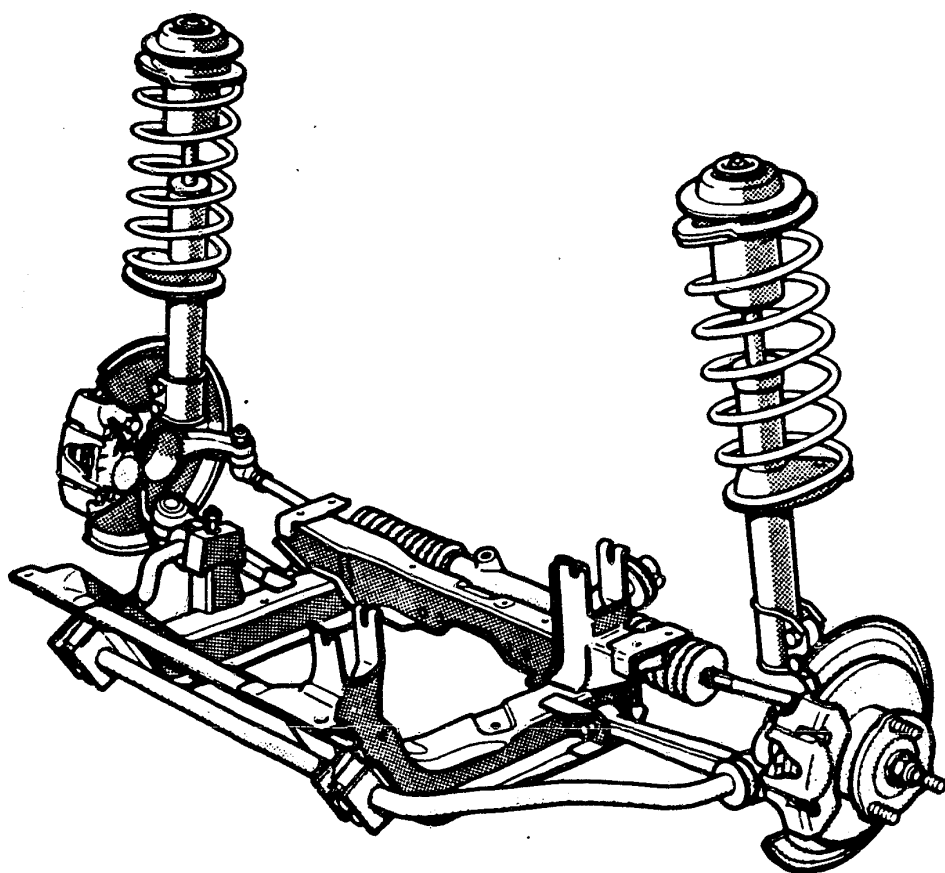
Vorderradaufhängung mit Motortragrahmen.
